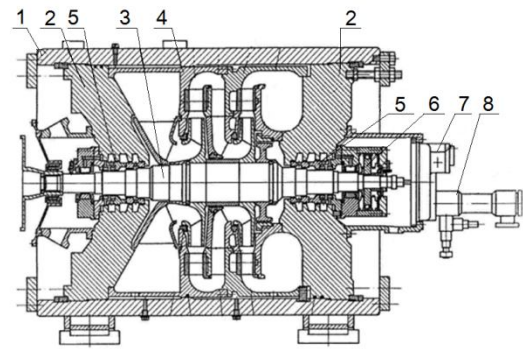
Відцентровий компресор НЦ-16/76-1,44 потужністю 16 МВт агрегату ГПА-Ц-16/76-1,44:1 – корпус; 2 – кришки корпусу; 3 – ротор; 4 – статорні елементи; 5 – кінцеві ущільнення ротора; 6 – мастильні підшипники; 7 –насос системи змащення; 8 – мастильний насос системи ущільнення
